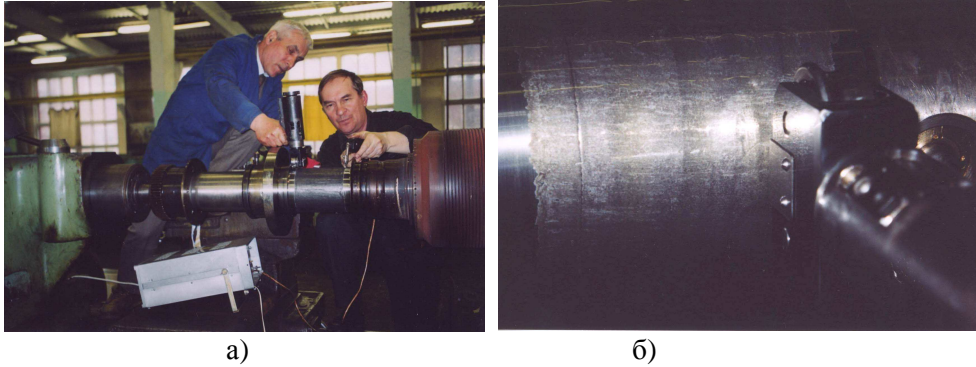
ЭЭЛ (а) и ОШ (б) подшипниковой шейки ротора турбокомпрессора ГТТ-3
